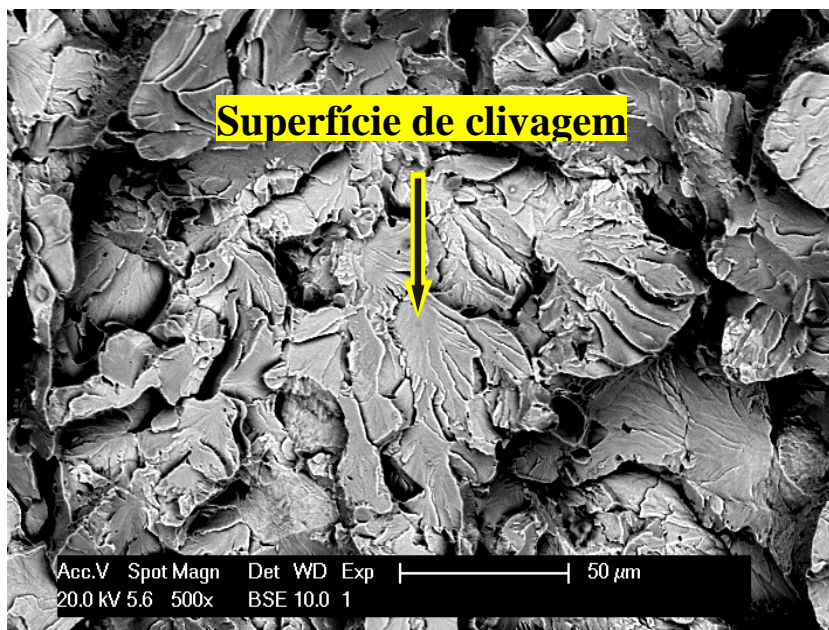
Fractografia da região final da ruptura no metal de base da liga não soldável. Superfície de fratura com aspecto de clivagem, indicando fratura frágil.
